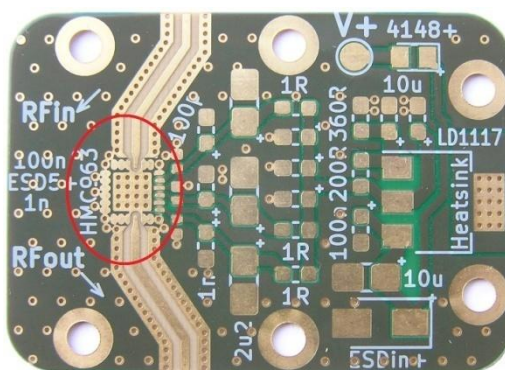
Hotový panel z PragoBoardu (MT-77, ENIG)
